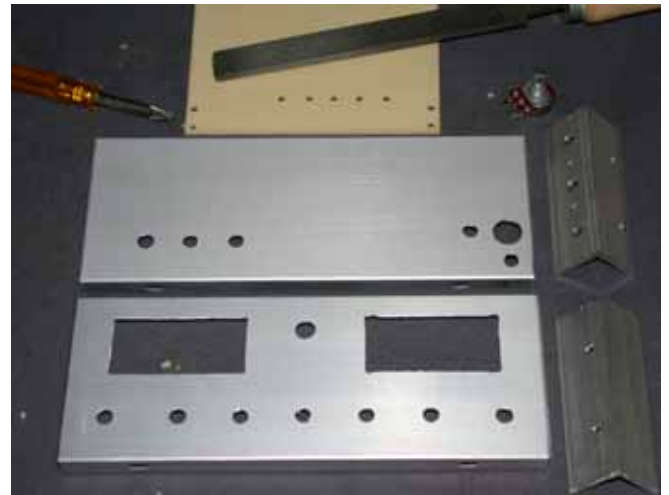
PC 鑽孔後開始小心焊接零件
